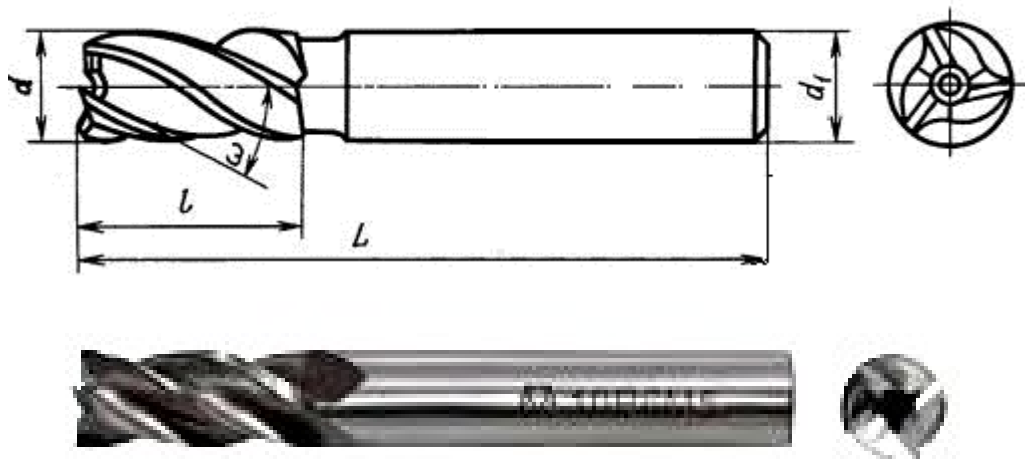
Кінцева фреза для нарізування шліців
